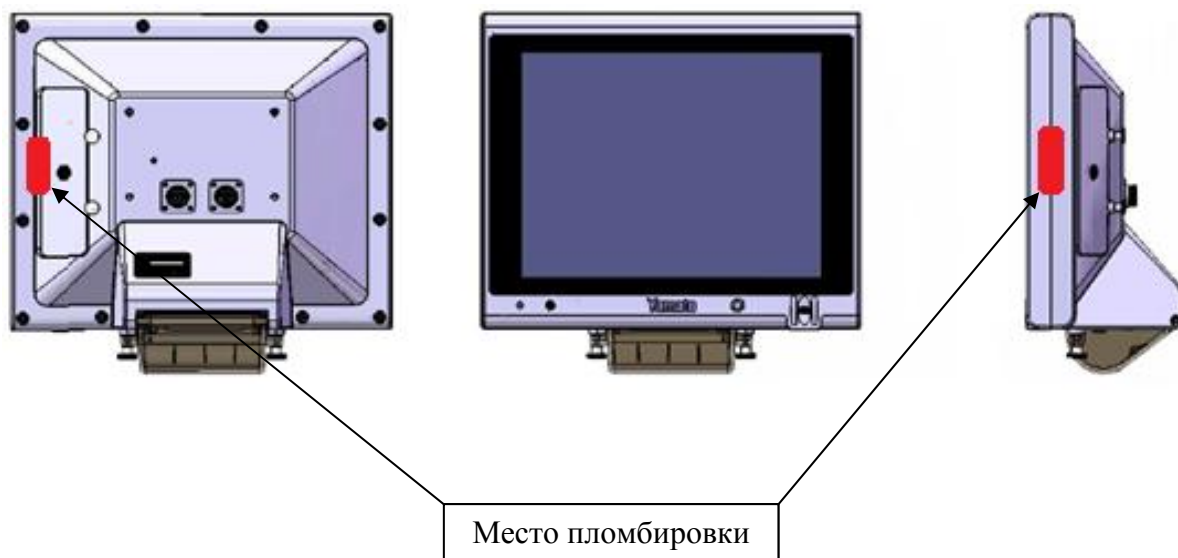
Пломбировка корпуса индикатора RCU-1000
